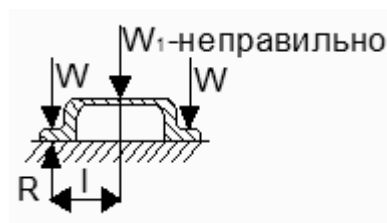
Схемы расположения сил зажима на заготовке.
